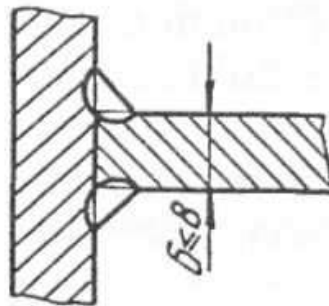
Вид зварного з'єднання лапи з плитою.
